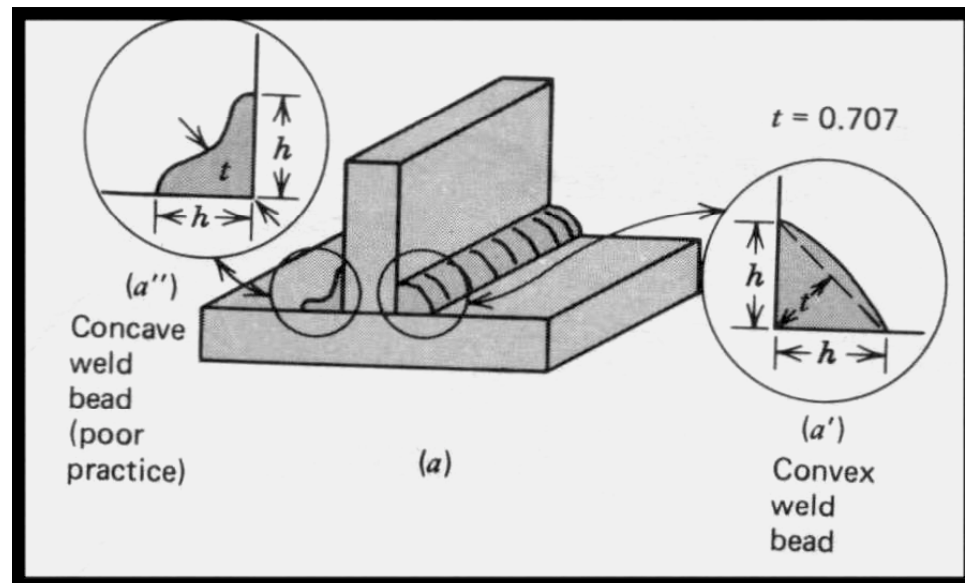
Filetes de Solda em Viga T invertida e Detalhes mostrando as dimensões, a forma correta de soldagem (à direita) e a incorreta (à esquerda)
